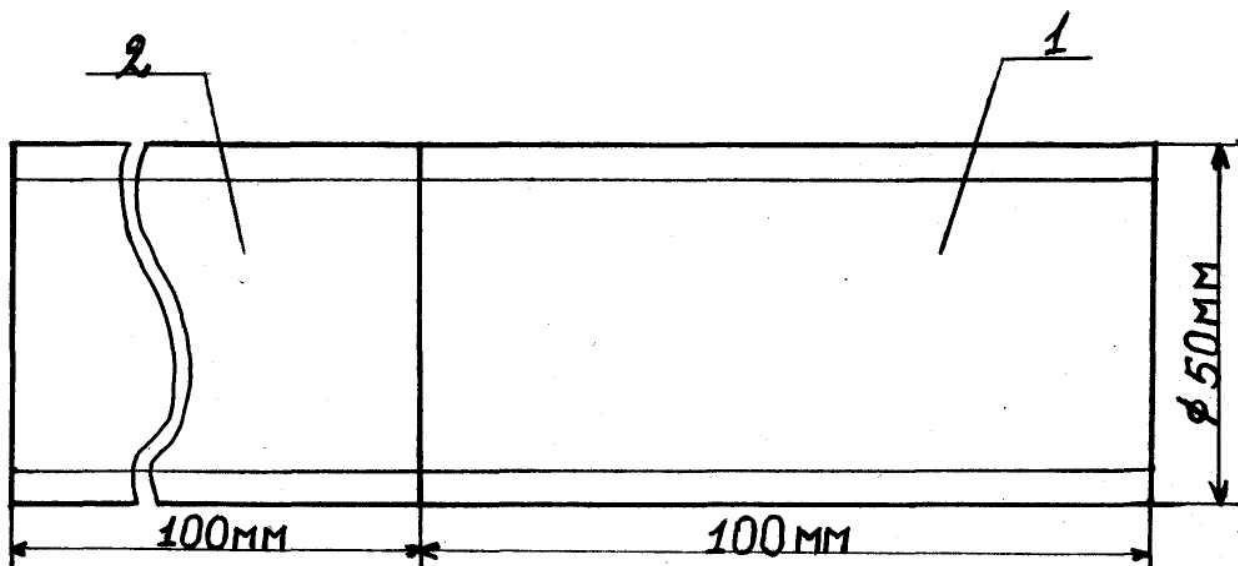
Эскиз сварки труб поворотным способом
